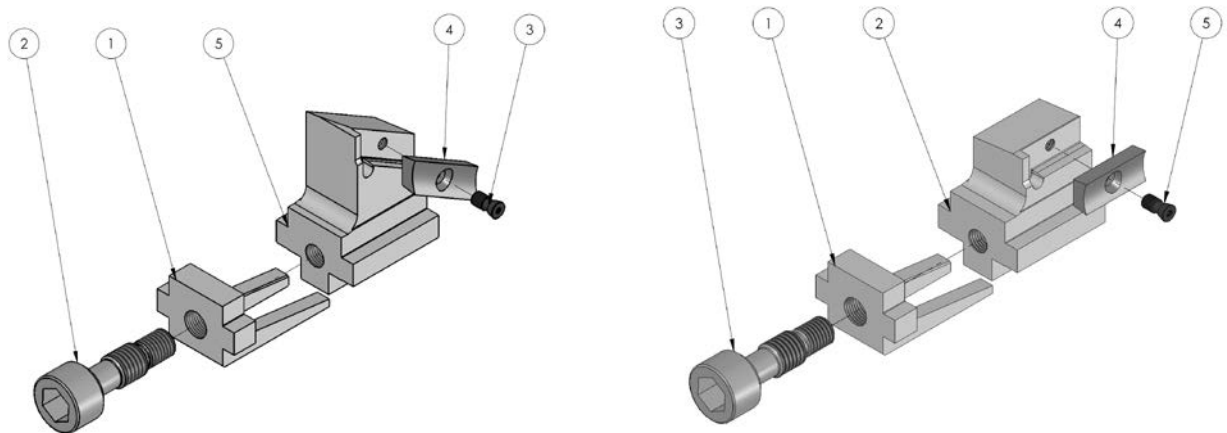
1 – клиновой запор; 2 – фиксирующий винт; 3 – винт пластины; 4 – пластина режущая
